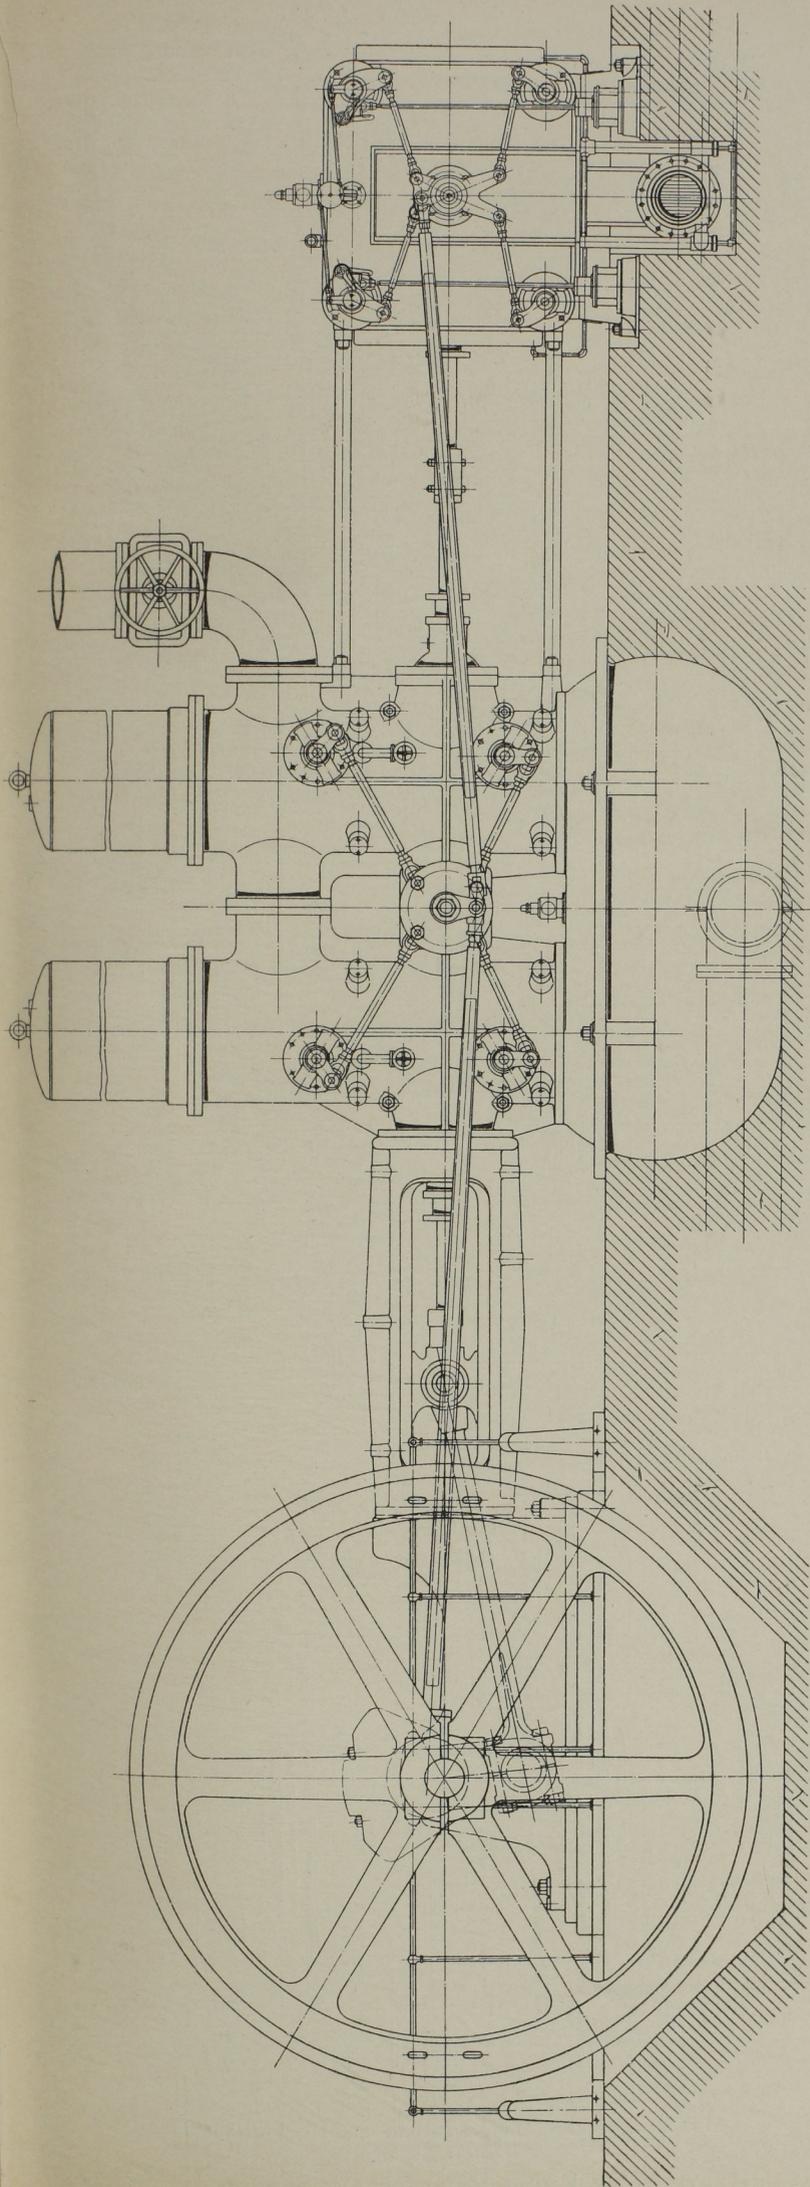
Seitenansicht der Hochdruckpumpe. Massst. 1 : 48.
